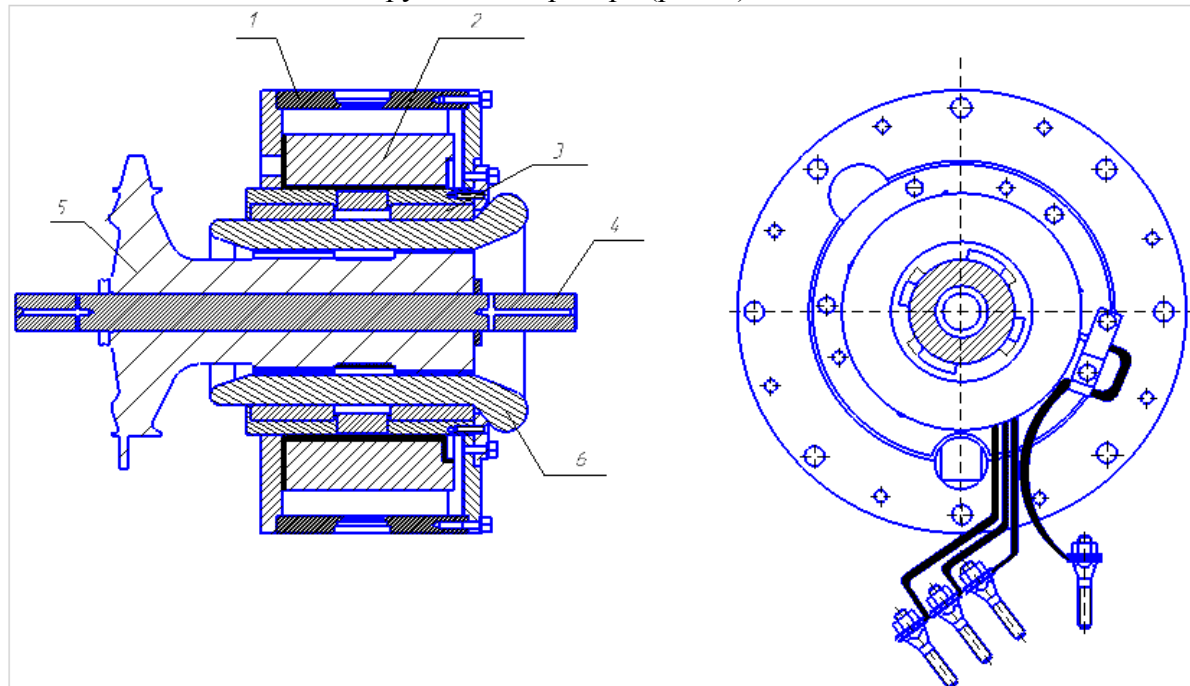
Конструкция генератора ОАО “ТЭМЗ”: 1– корпус; 2 – обмотка возбуждения; 3 – пакет статора; 4 – вал; 5 – турбина (ротор); 6 – катушка статора
